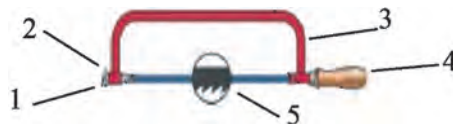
Ножовка для резки металла: 1 – передний узел крепления; 2 – натяжная гайка; 3 – рамка; 4 – рукоятка; 5 – ножовочного полотна.
